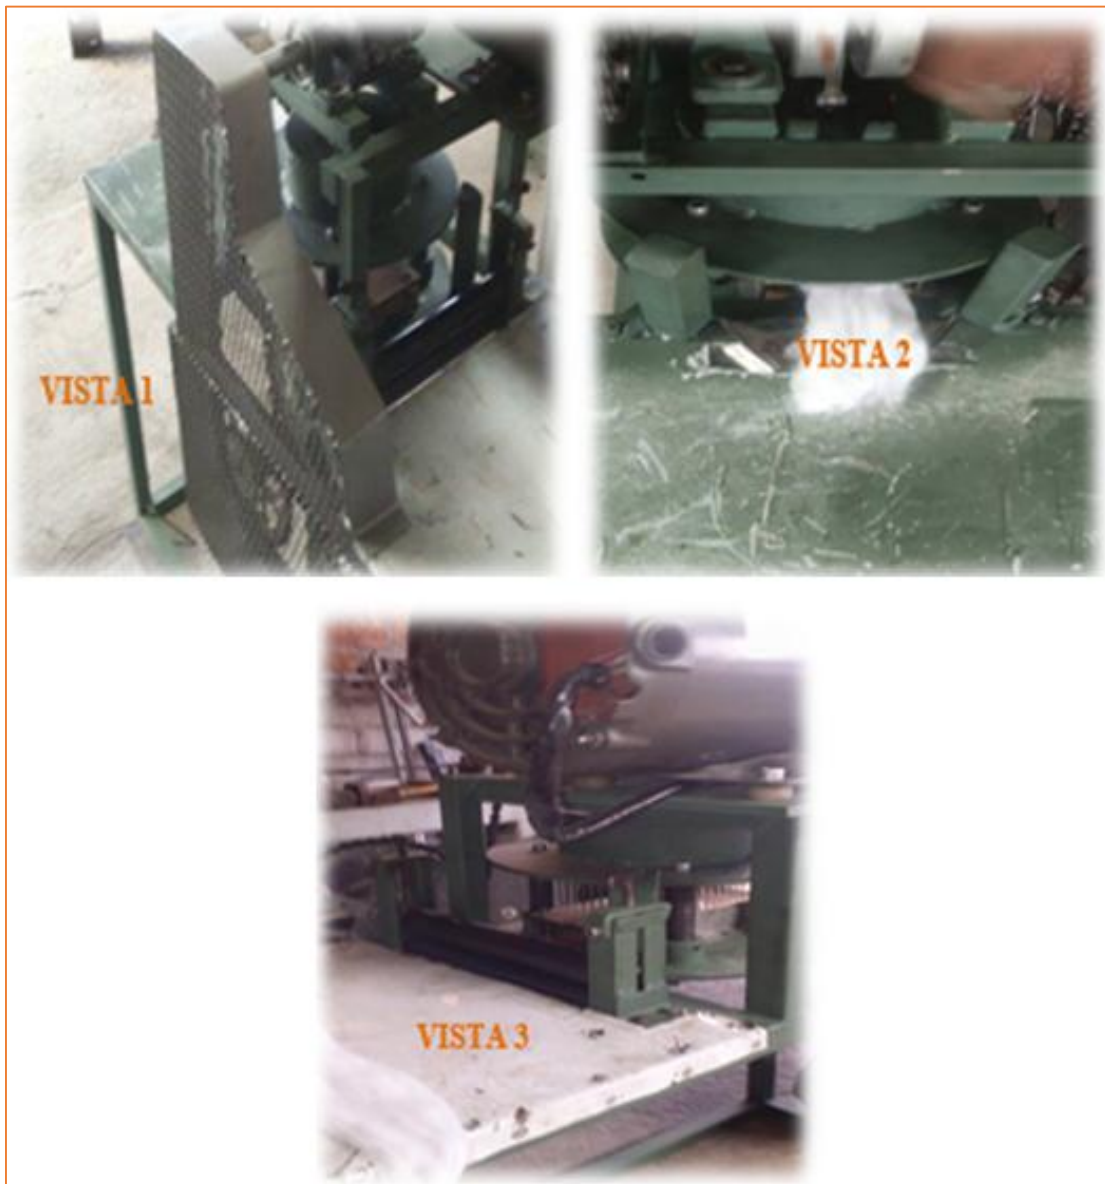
Vistas de la Máquina Punzonadora Terminada
